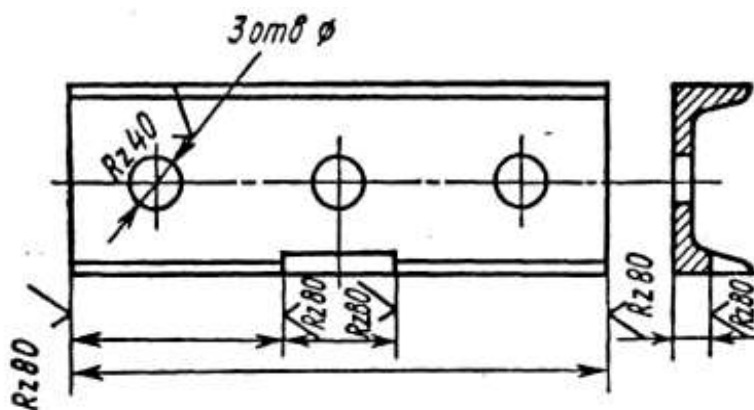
К обозначению шероховатости на отливках, поковках и т.д.
